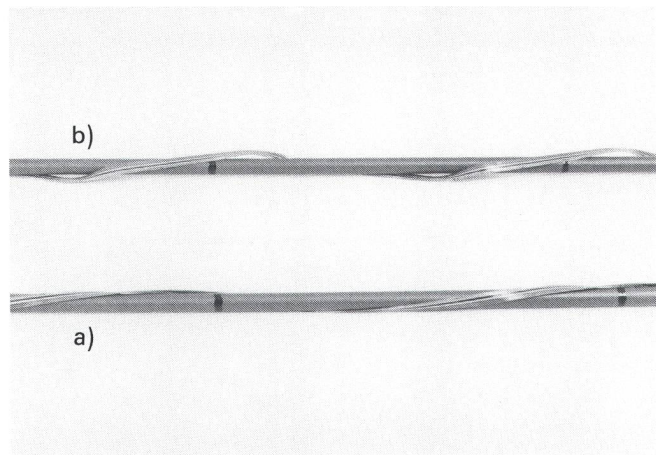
Variantes d'assemblage d'un ruban autour d'un élément central cylindrique
